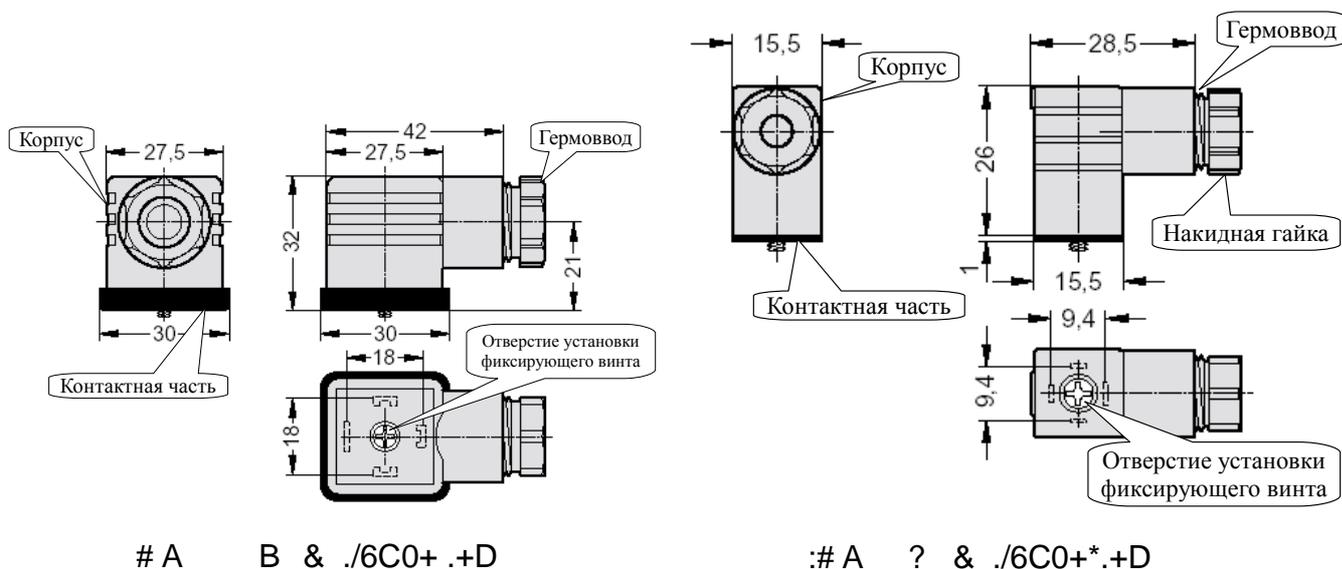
Соединитель электрический DIN 43650 (ISO 4400)
